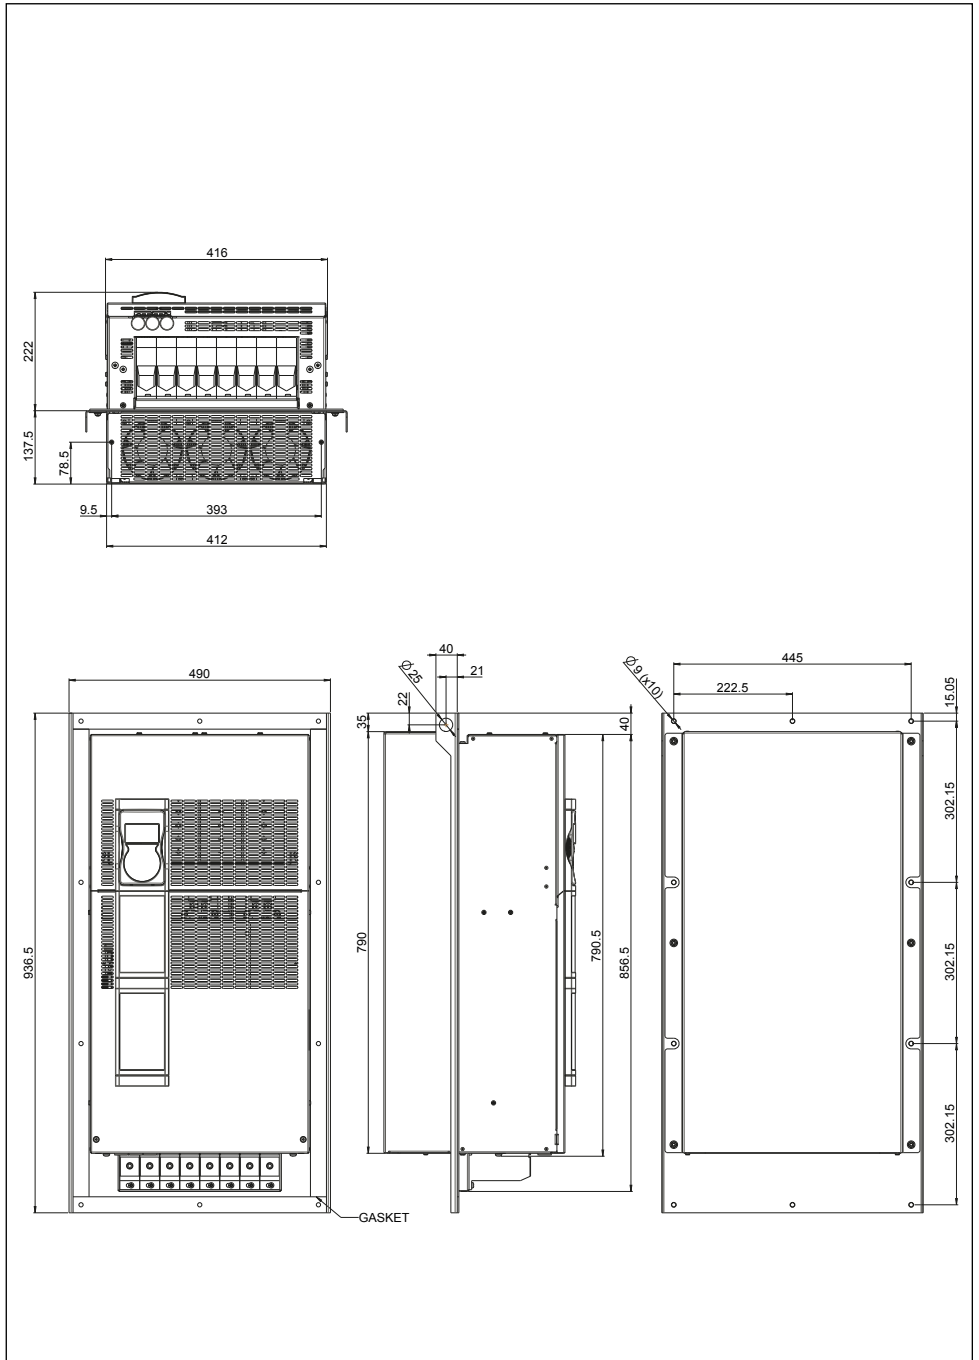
Размеры для типоразмера 2 (ADV200-...-EHR)
